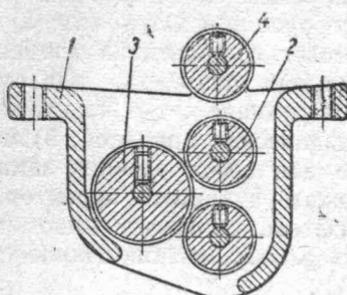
Противопожарный канал в разрезе: 1 — корпус; 2 — ролик; 3 — ролик; 4 — ось
